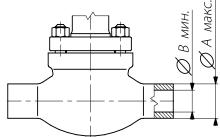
Размеры выводов для сварки, изготовленных из отливки.
